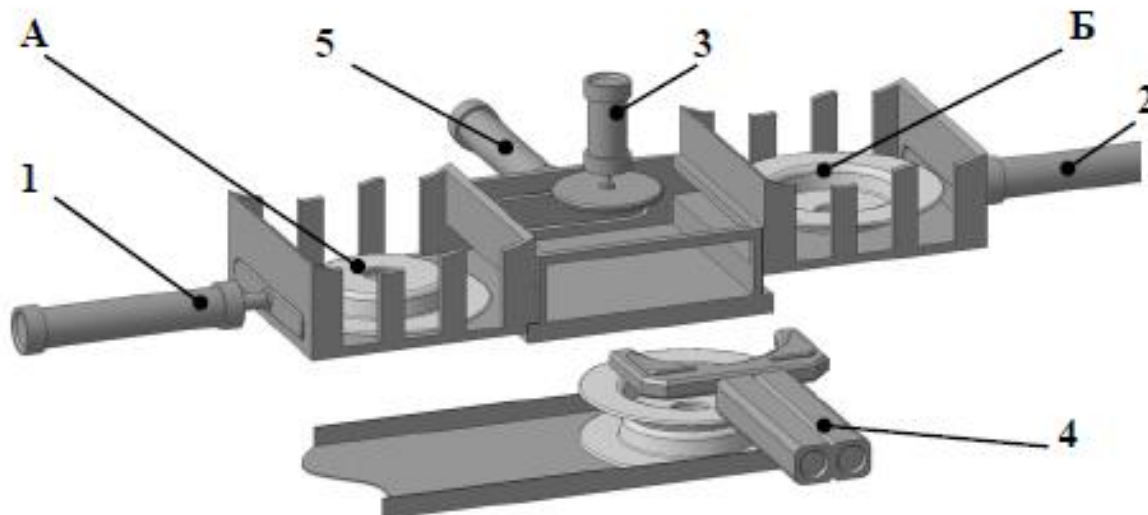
Конструктивна схема гідравлічного приводу зварювального автомата
